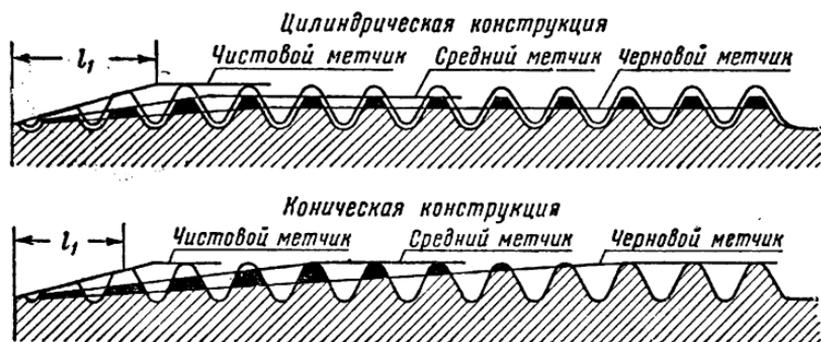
Схема продольных разрезов профилей цилиндрической и конической конструкций метчиков.
